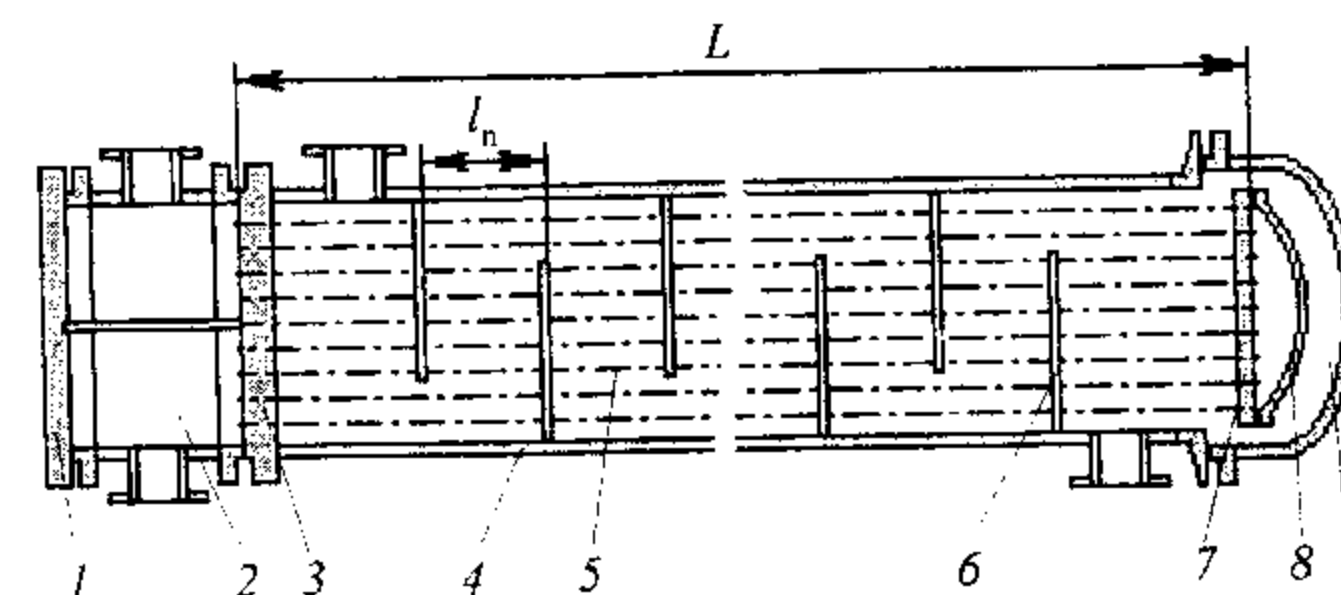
Кожухотрубчатый холодильник с плавающей головкой:
